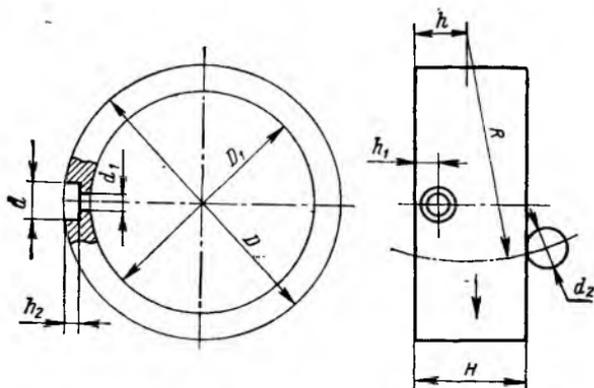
Заготовка кулачка осевой подачи руки-переносчика
